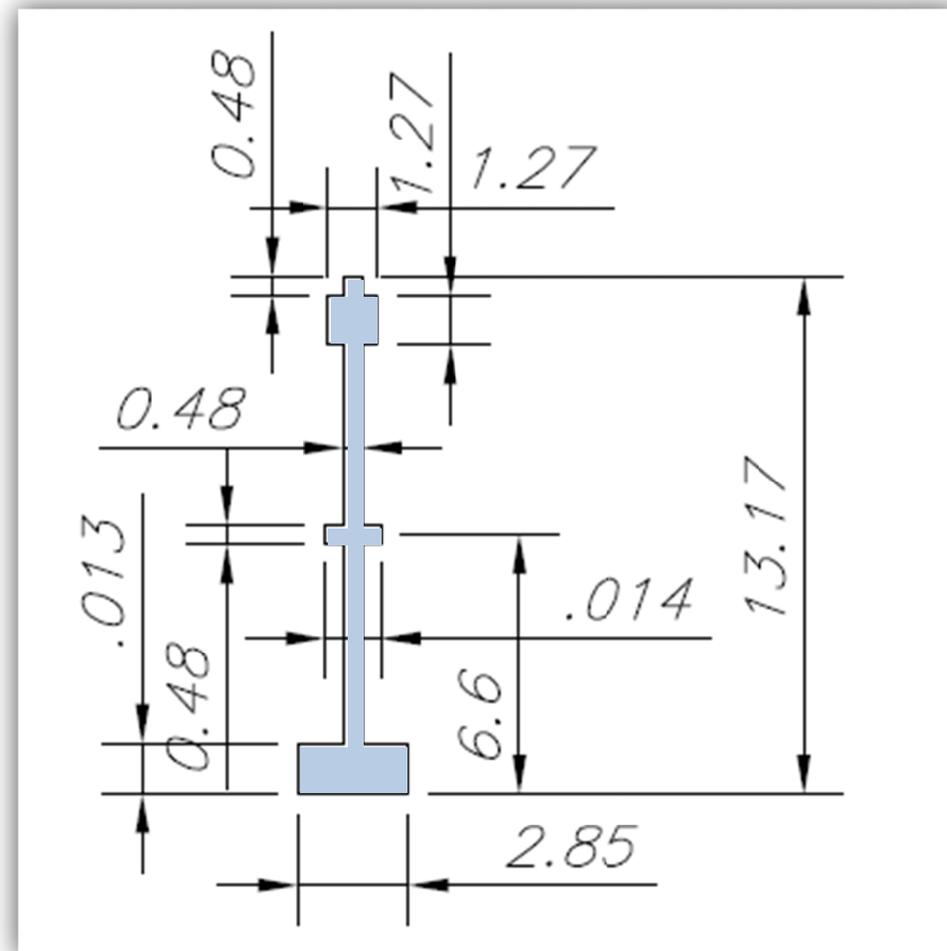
Sección transversal de la viga principal de la rejilla (distancias en cm)
